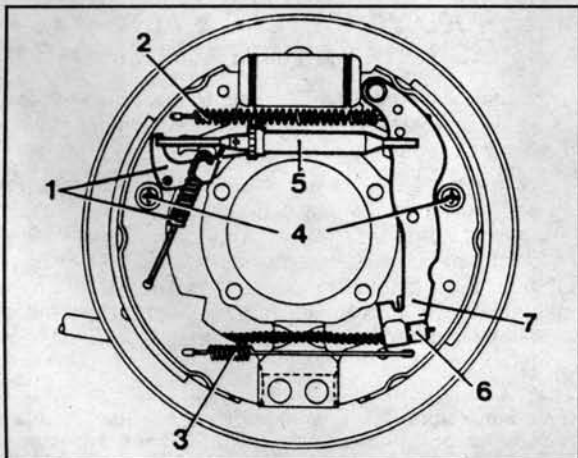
Тормоз заднего колеса автомобилей с двигателями В19, В200
